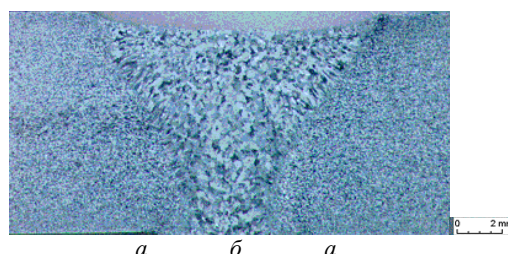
Структура сварного соединения листов из сплава АМг5:
